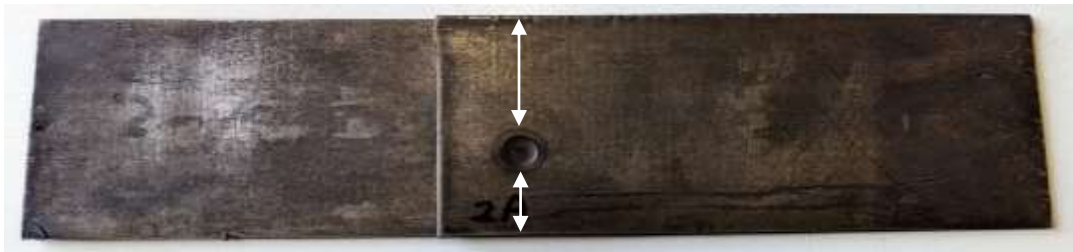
Muestra A2 soldada fuera del centro de la lámina.
